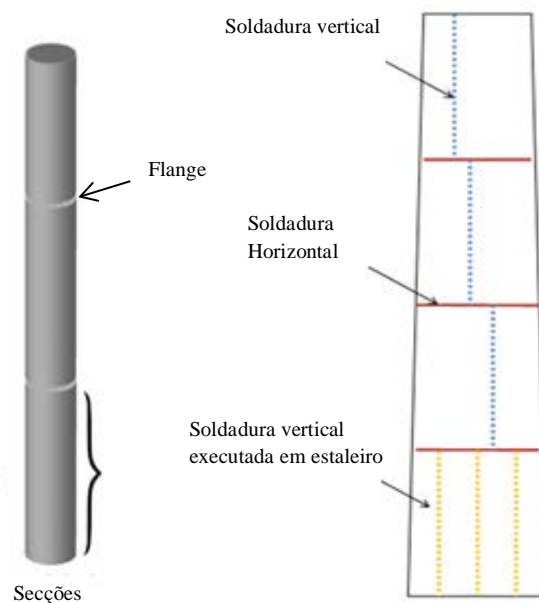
Ilustração sobre construção de torres eólicas soldadas [12].
